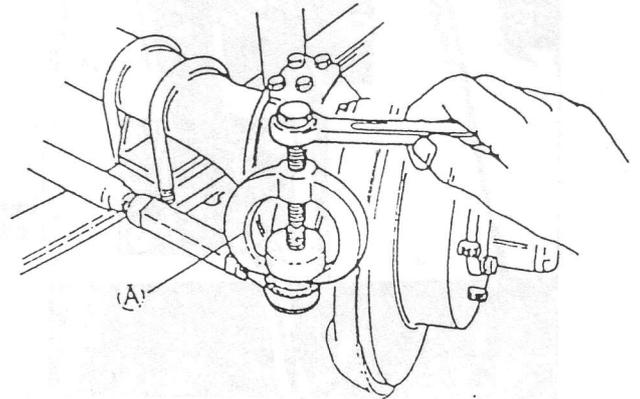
(A) Herramienta especial (Extractor del extremo de la barra de acoplamiento 09913-65210).
